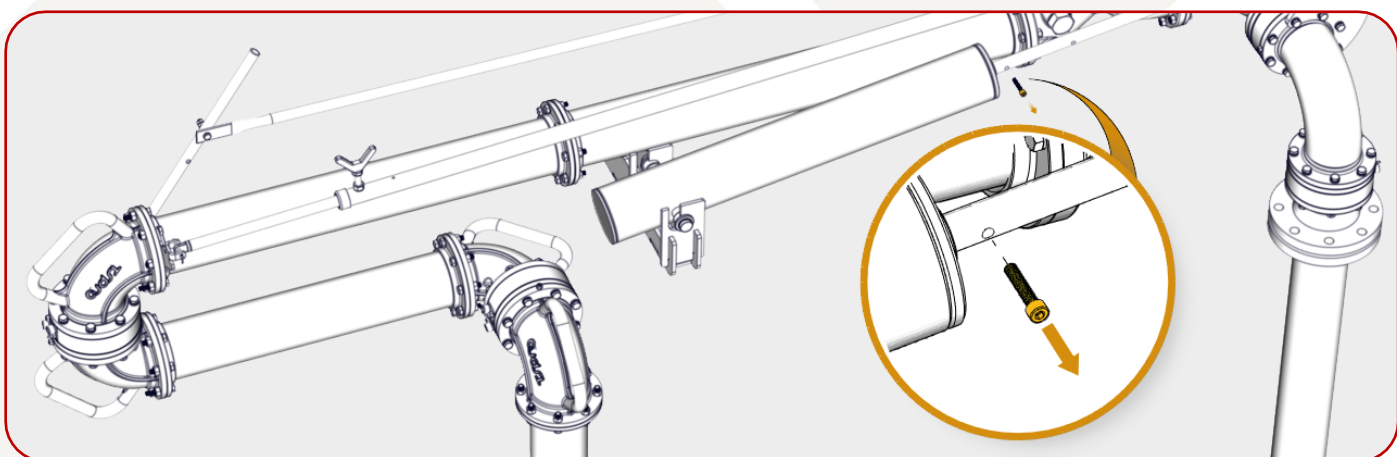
Retirar o Parafuso de Trava do Conjunto de Mola
